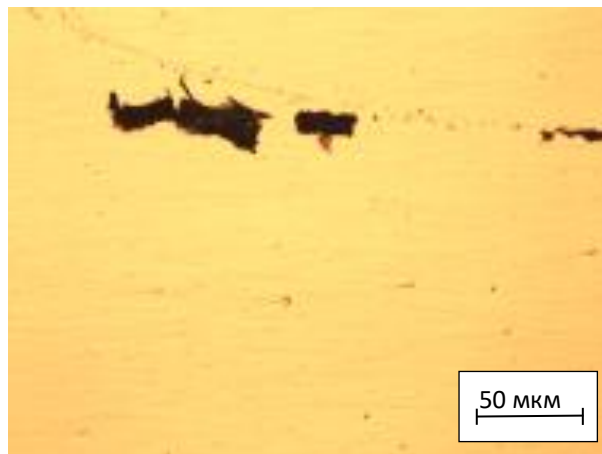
Шлаковые включения в сварном шве
